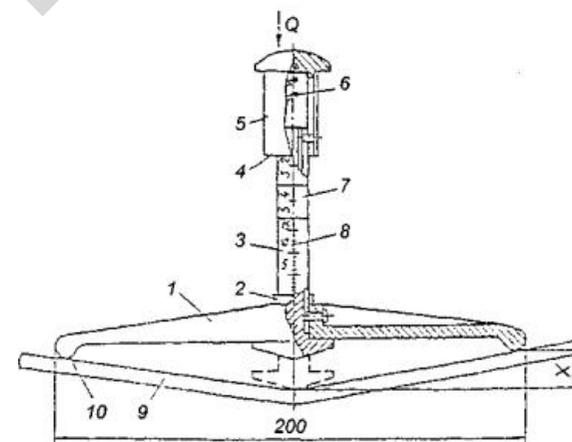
Приспособление для контроля натяжения ремней:
